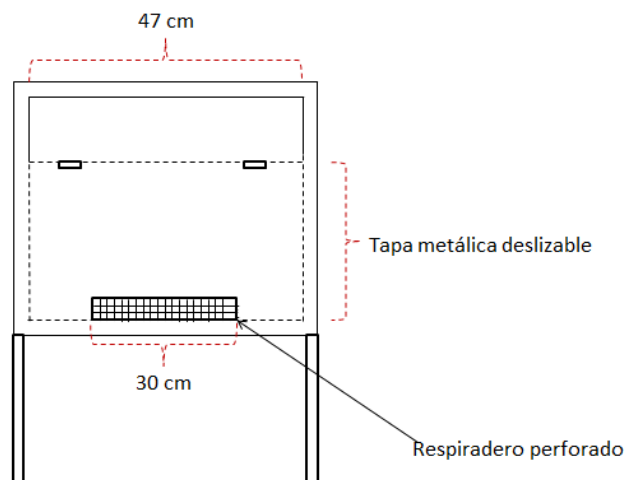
Dimensiones del deshidratador de 3kg parte frontal delantera.
